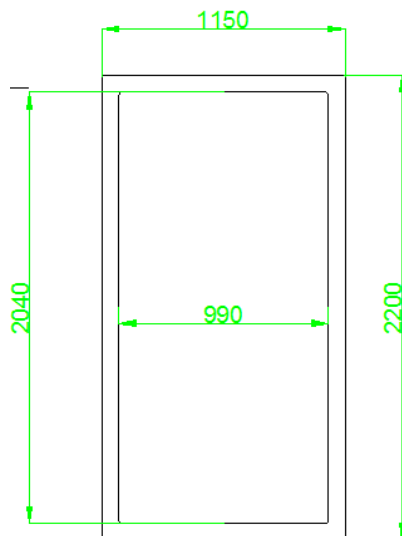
Dimensiones externas del frontal de la cabina
